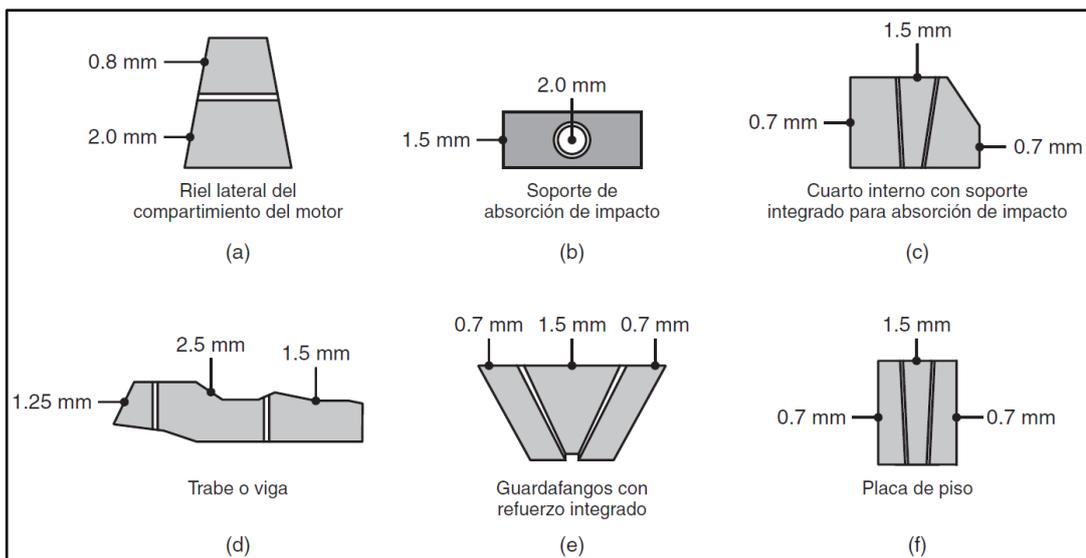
Ejemplos de componentes de carrocería automotriz soldados a tope con rayo láser y estampados.
